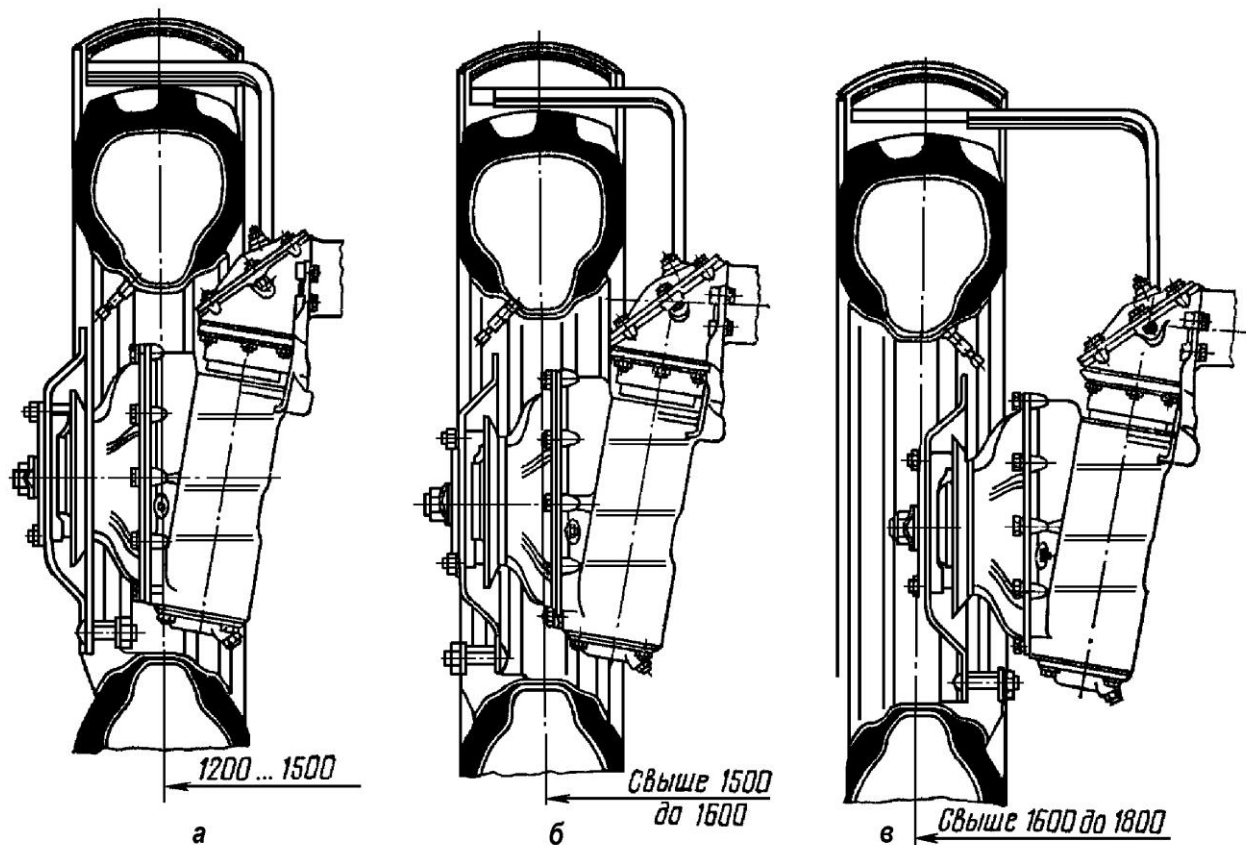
Схема установки передних колёс трактора МТЗ-82
